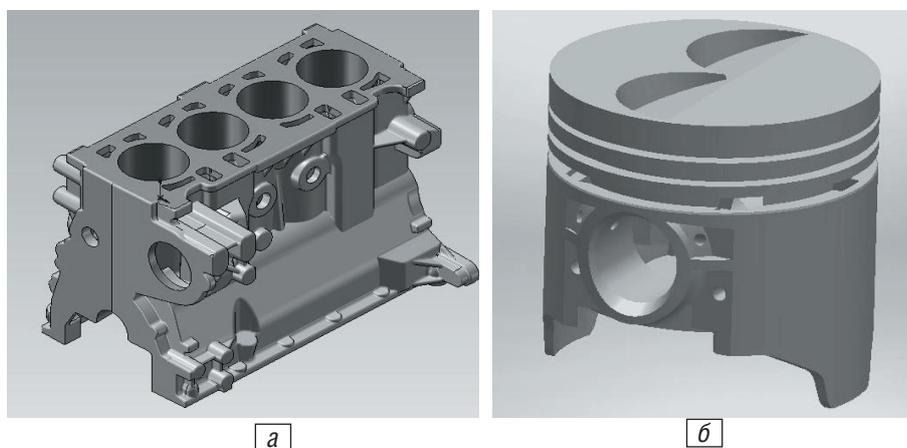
3D-модель: блока цилиндров (а); поршня (б)
